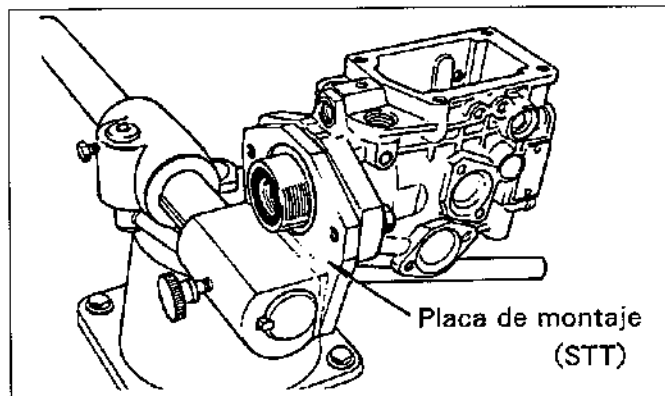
Montaje de la bomba en la placa de montaje (STT)
